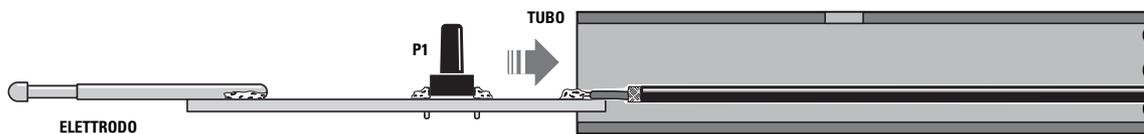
primeramente insertad la pieza del circuito en el impreso dentro del tubo, como se ve en el dibujo.
